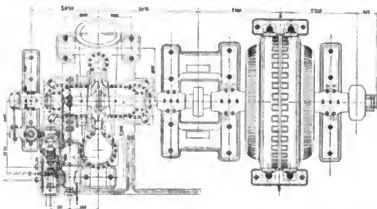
Grundriß einer 6000 PS-Maschinengruppe Manojlovac.
